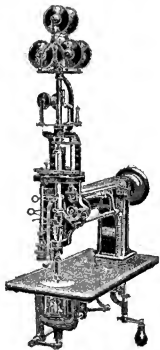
Universal-Stick-Maschine „Stella“ von G. Stein, Berlin.
